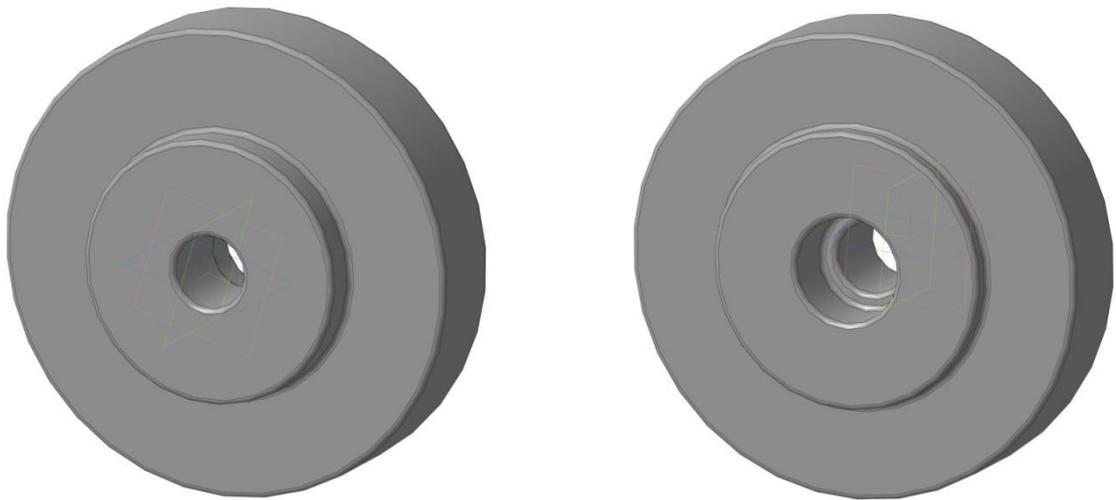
3D модель заготовки для детали «Крышка передняя»
